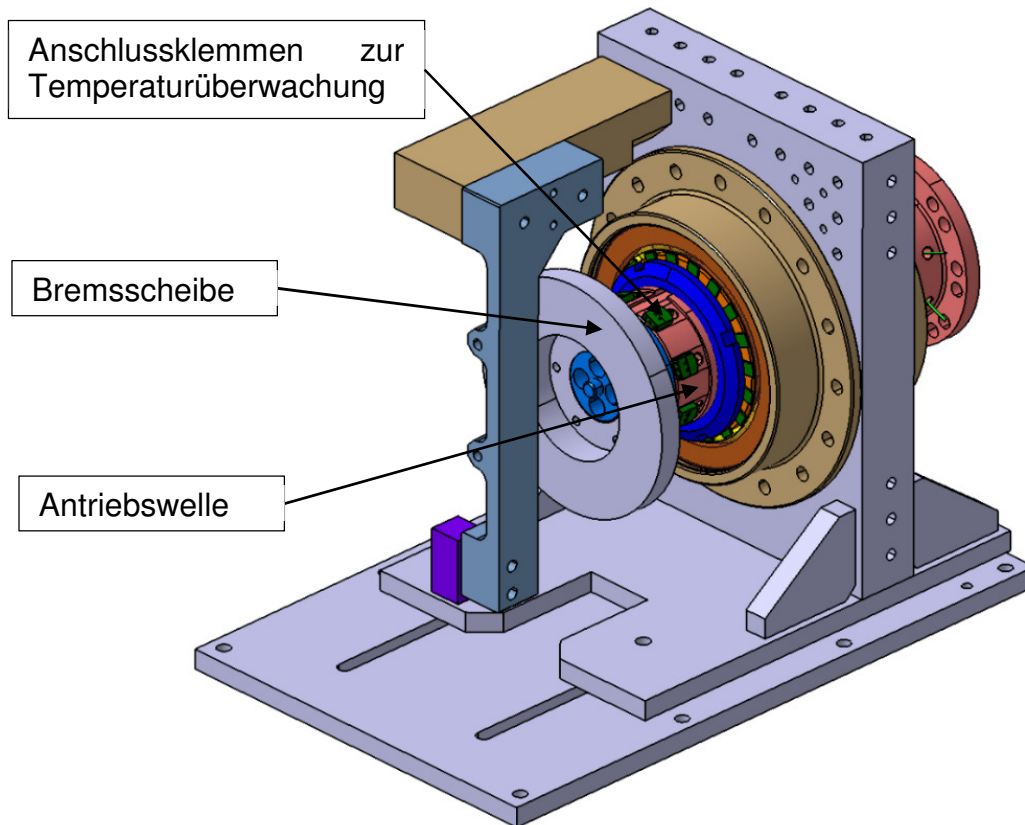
Grundaufbau des bestehende Adapters zur Bremsenprüfung
